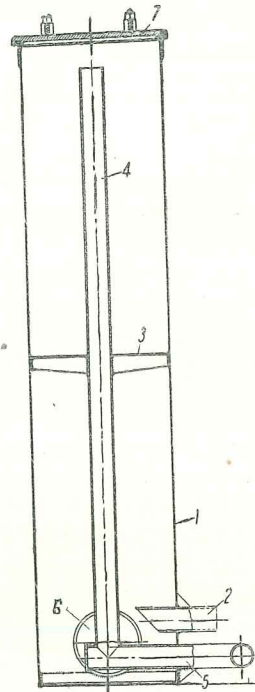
Схема газоочистителя установки ЛТА для автомобиля ЗИС-5
